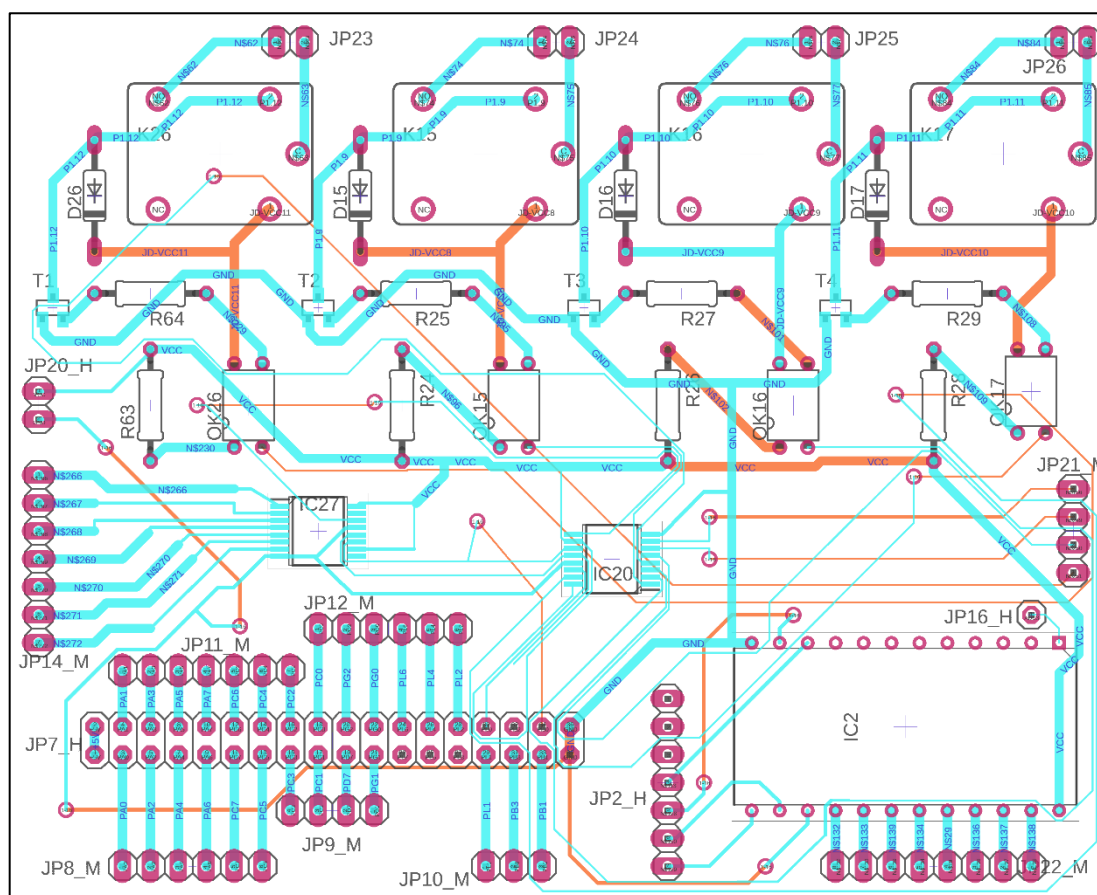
Diseño del circuito impreso del prototipo comercial (primera parte de la placa). (Fuente: elaboración propia)
